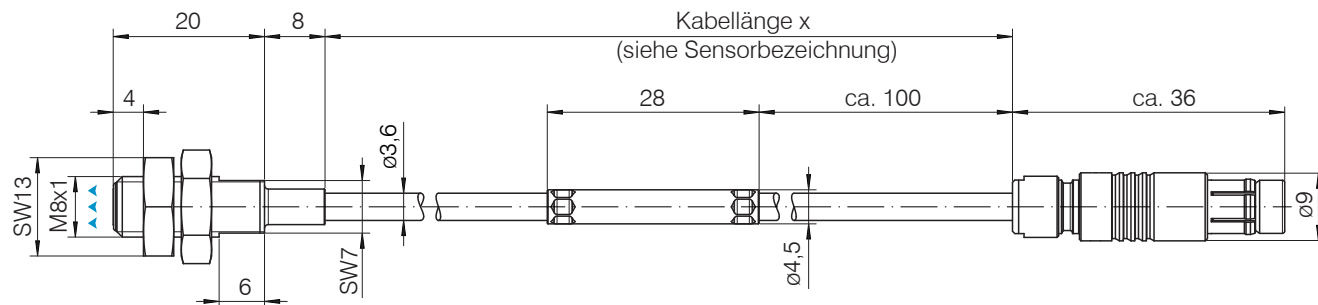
Maßzeichnung Sensoren ES-S1-C-CAx/mB0, Abmessung in mm
